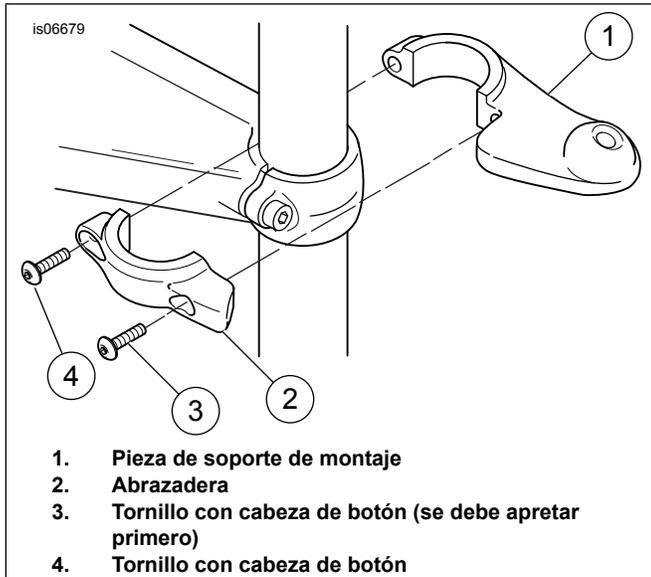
Instalación de la pieza de soporte de montaje en el tubo de la horquilla (se muestra el lado derecho)
